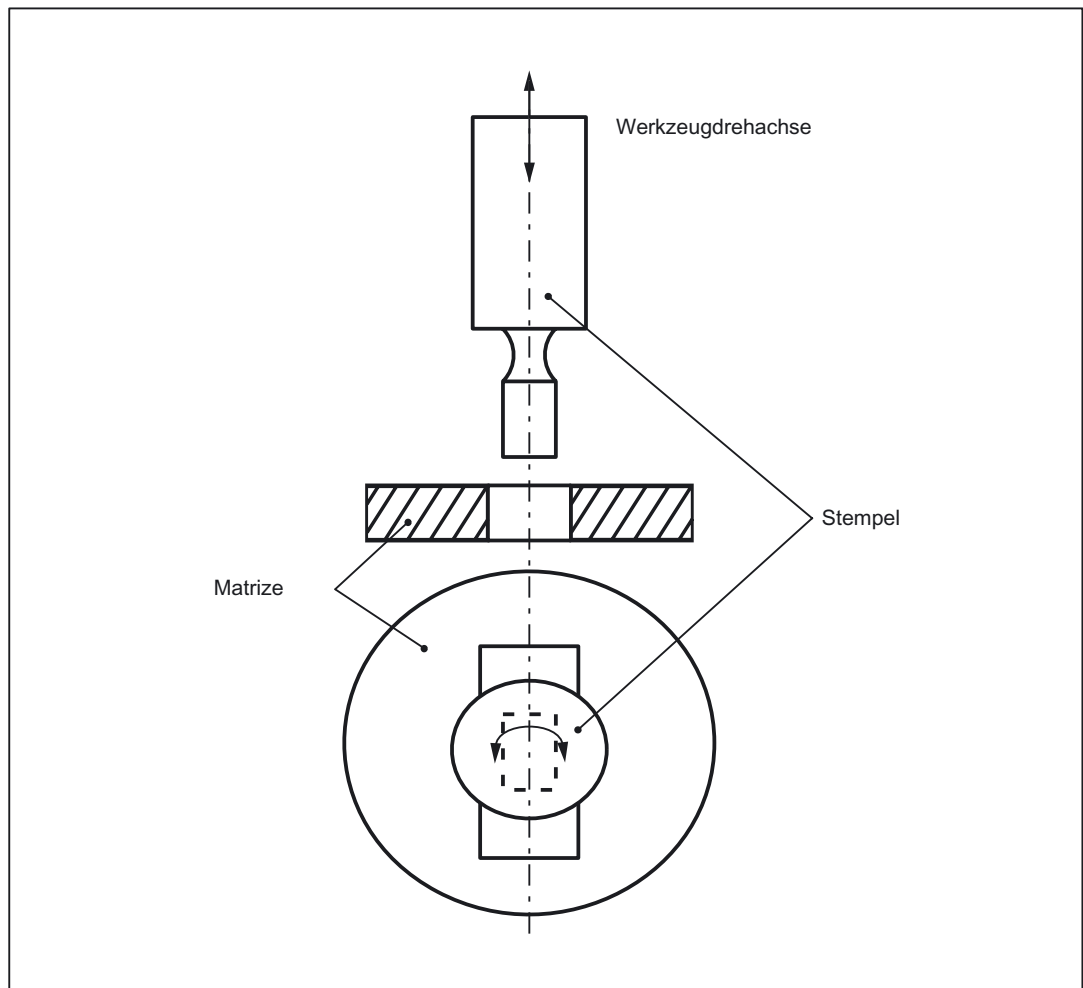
Darstellung einer drehbaren Werkzeugachse
